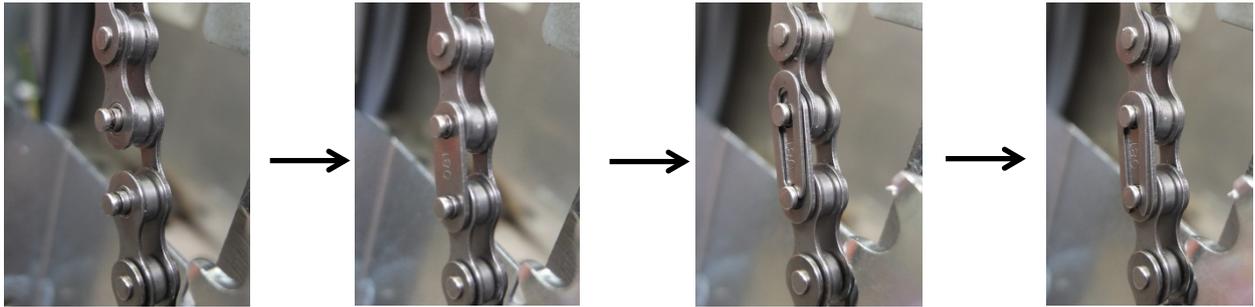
Montagefolge Kettenschloss / pict. 10: assembly sequence chain lock
